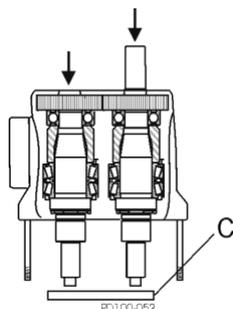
Herausdrücken der Wellen aus dem Getriebegehäuse
